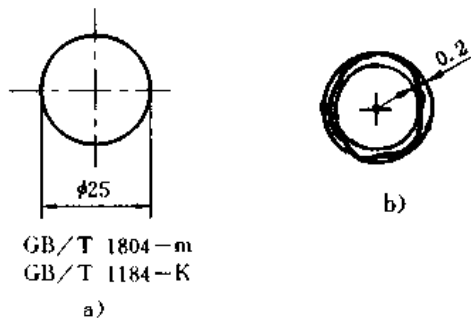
圆度未注公差值等于径向圆跳动公差值
